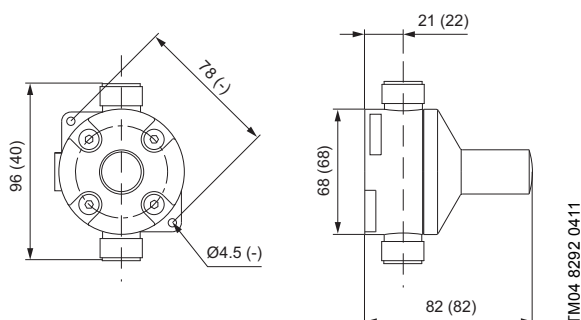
Нагнетательный клапан. Размеры, указанные в скобках, относятся к исполнению из нержавеющей стали.
